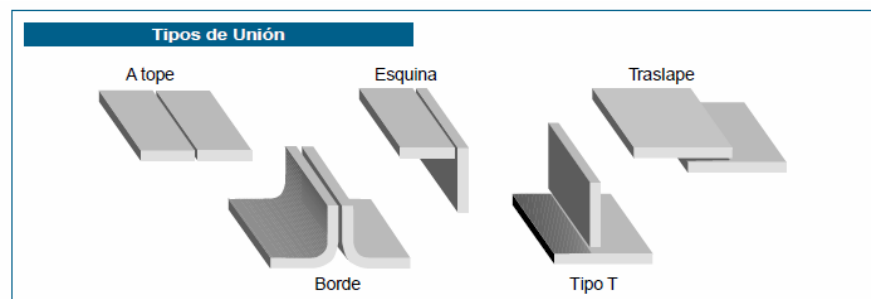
Tipos de uniones en soldadura
